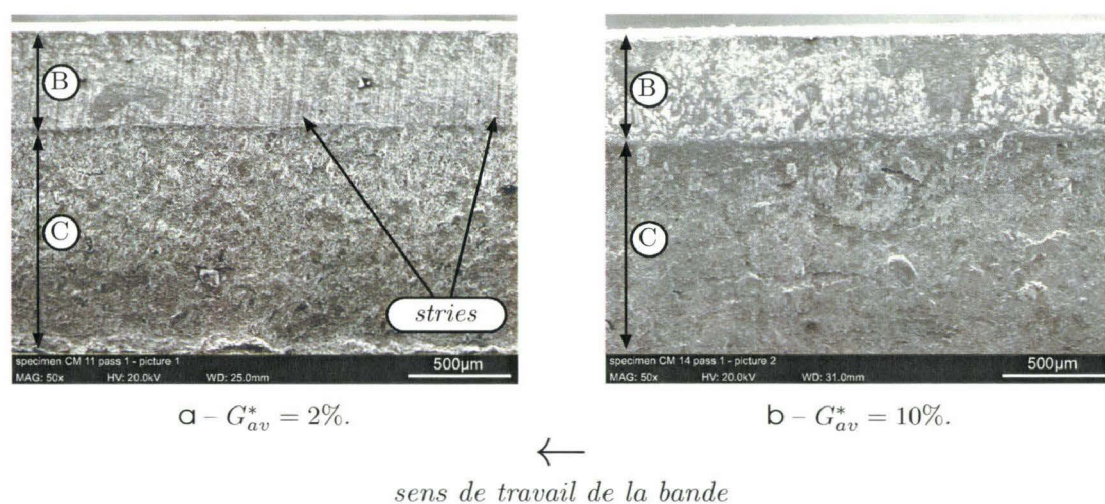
Observations au MEB des rives après la première passe de déformation (éprouvettes TH).
